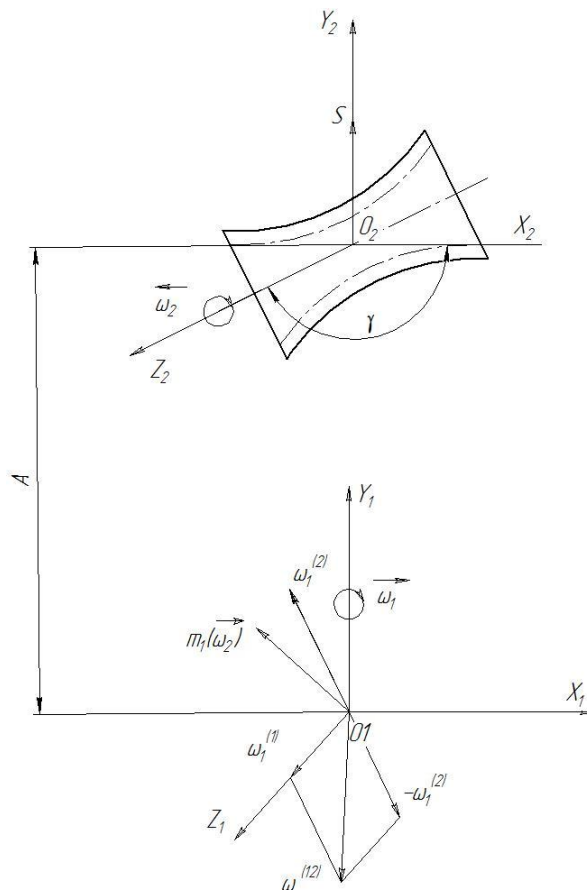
Схема расположения векторов угловых скоростей при притирке зубьев зубчатых колес
